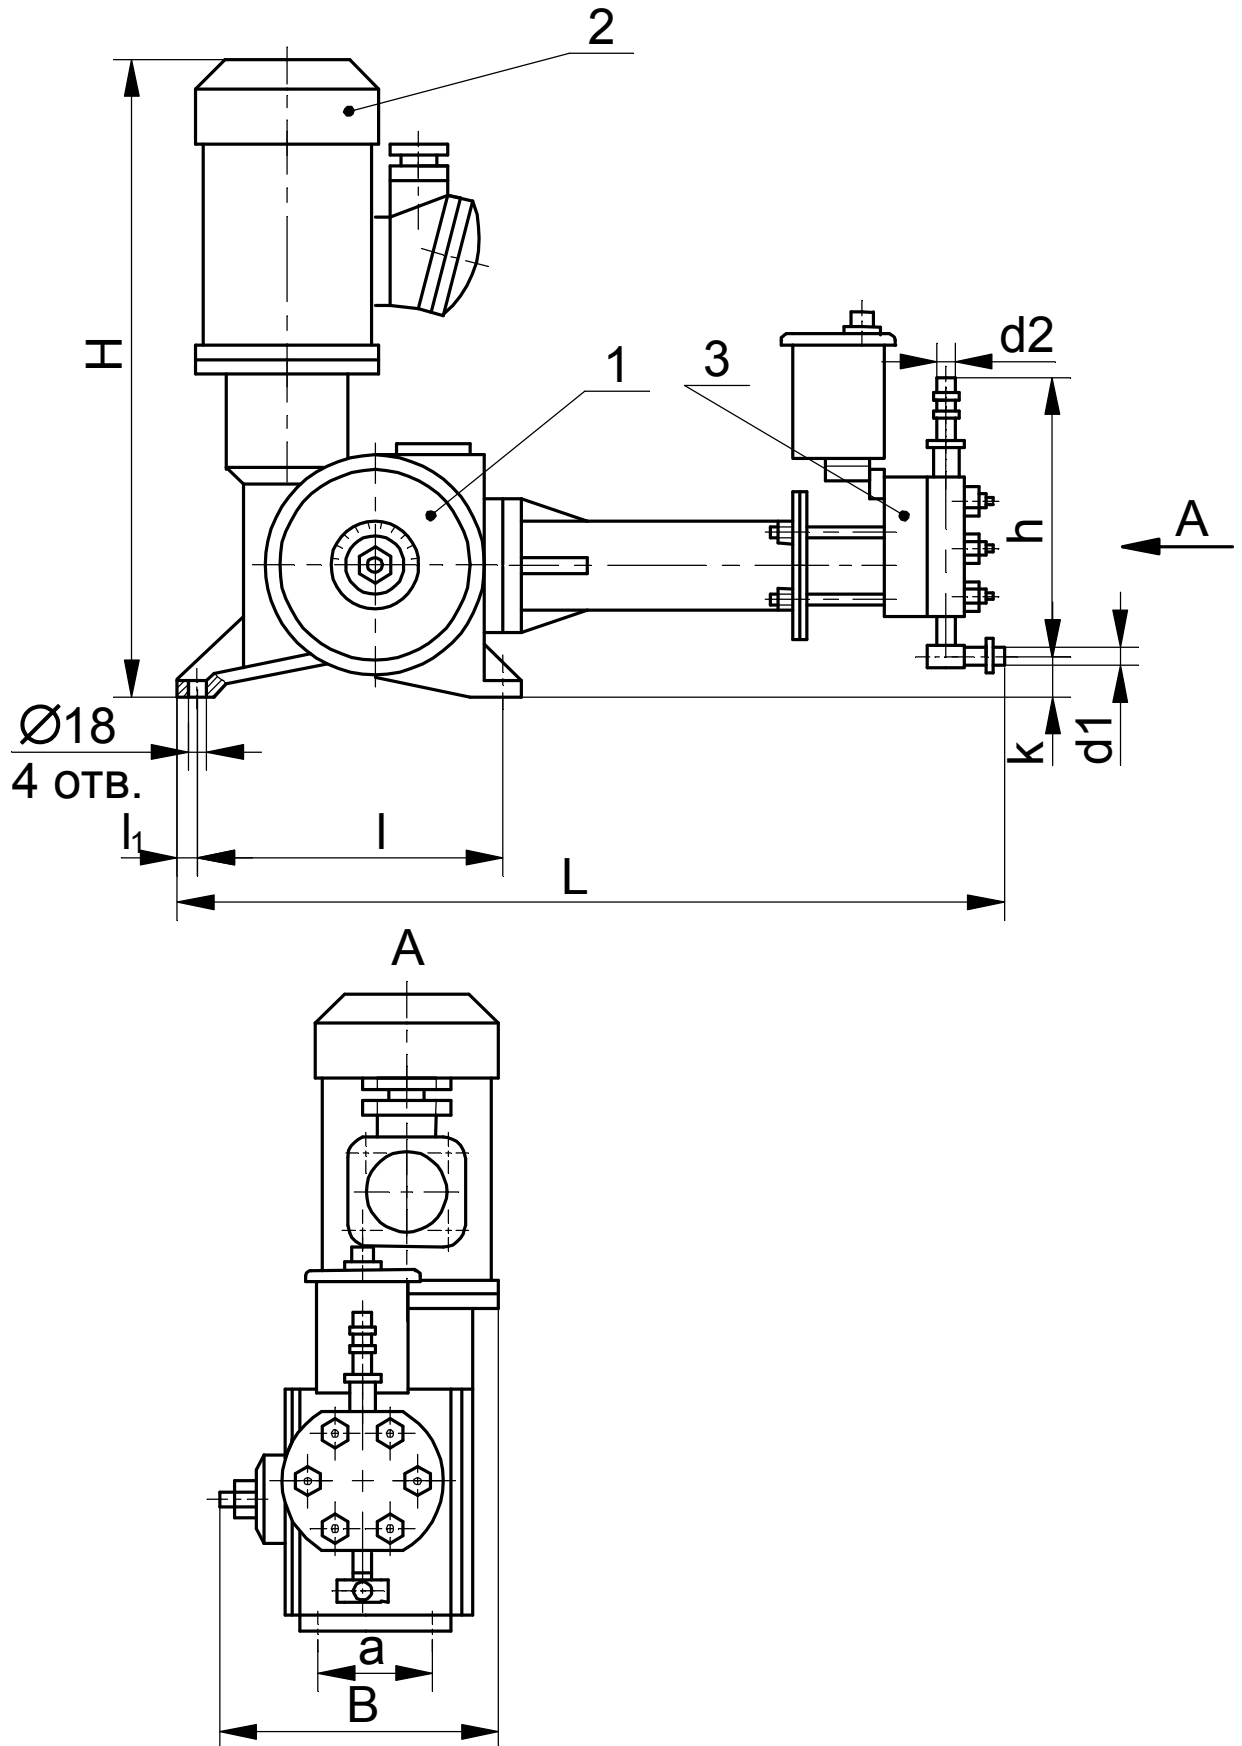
Внешний вид агрегата с параметрами номинального режима 25/250; 40/160; 63/100; 100/250 и 160/40. Габаритные и установочные размеры
